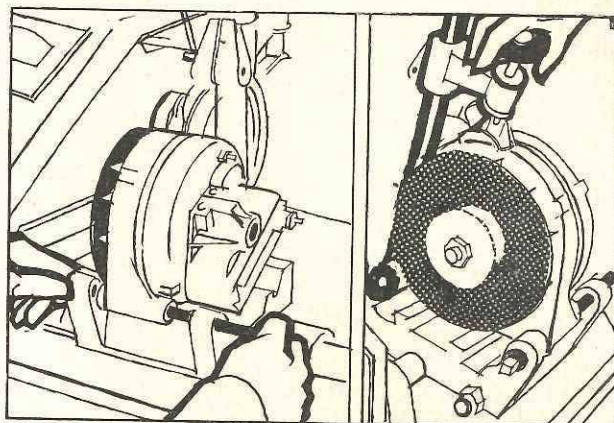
Drehstrom-Generatoren dürfen zum Prüfen meist nicht mit Druckspindeln auf Prismen eingespannt werden, weil sich dann das Weicheisengehäuse verziehen könnte. Darum werden diese Maschinen in ihrem Lagerflansch angeschraubt, und auch die Druckspindel darf nur auf den Lagerflansch gespannt werden.
